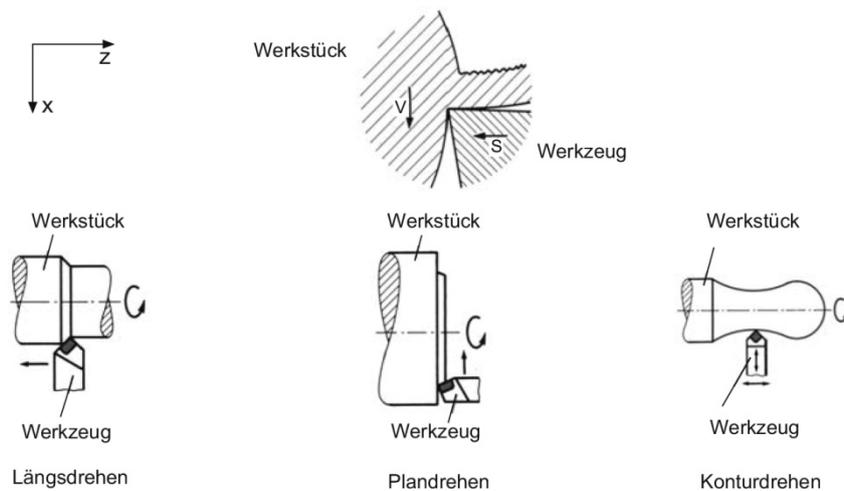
Drehen - Spanbildung - Dreharten; Quelle: Werkzeugmaschinen - Maschinenarten und Anwendungsbereiche, Springer
